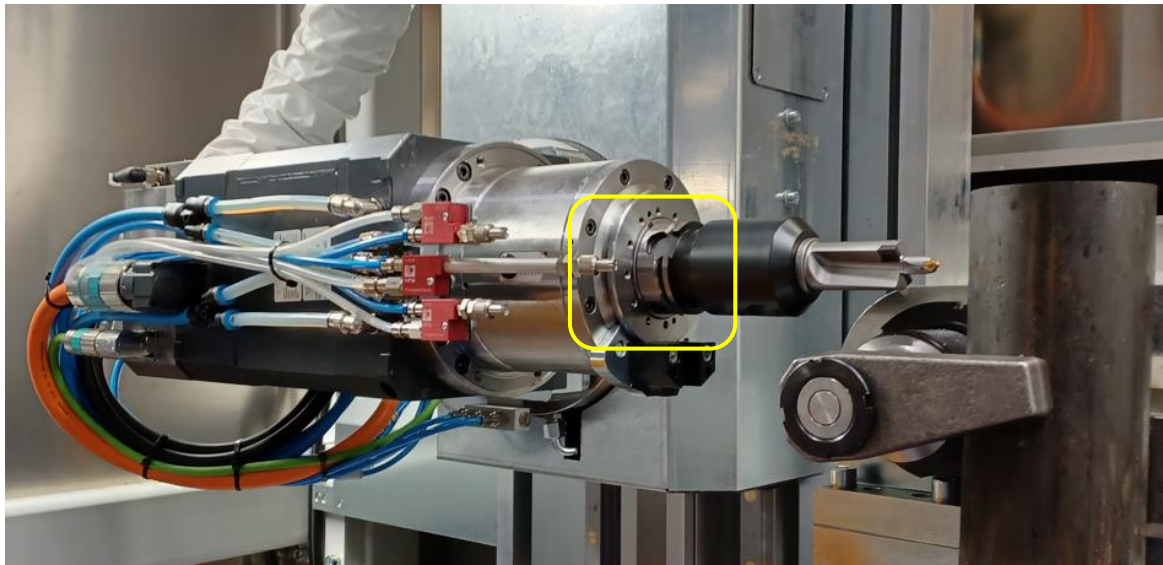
Bearbeitungsspindel mit HSK 63 Werkzeugaufnahme und Stufenwerkzeug
